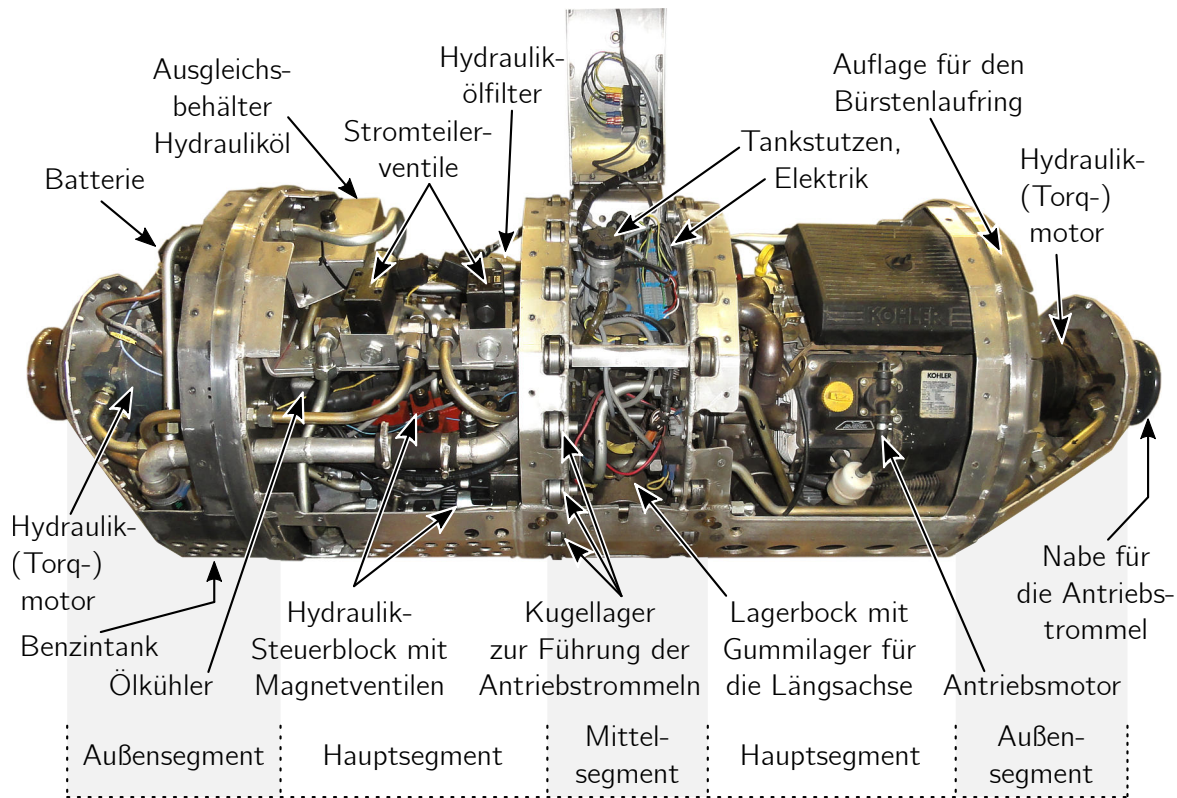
Innerer Aufbau der Q1-Antriebsachse mit demontierten Antriebstrummeln, hier mit dem Zweizylindermotor. Die Stromteilerventile werden in Abschnitt 4.1.2 erläutert.
